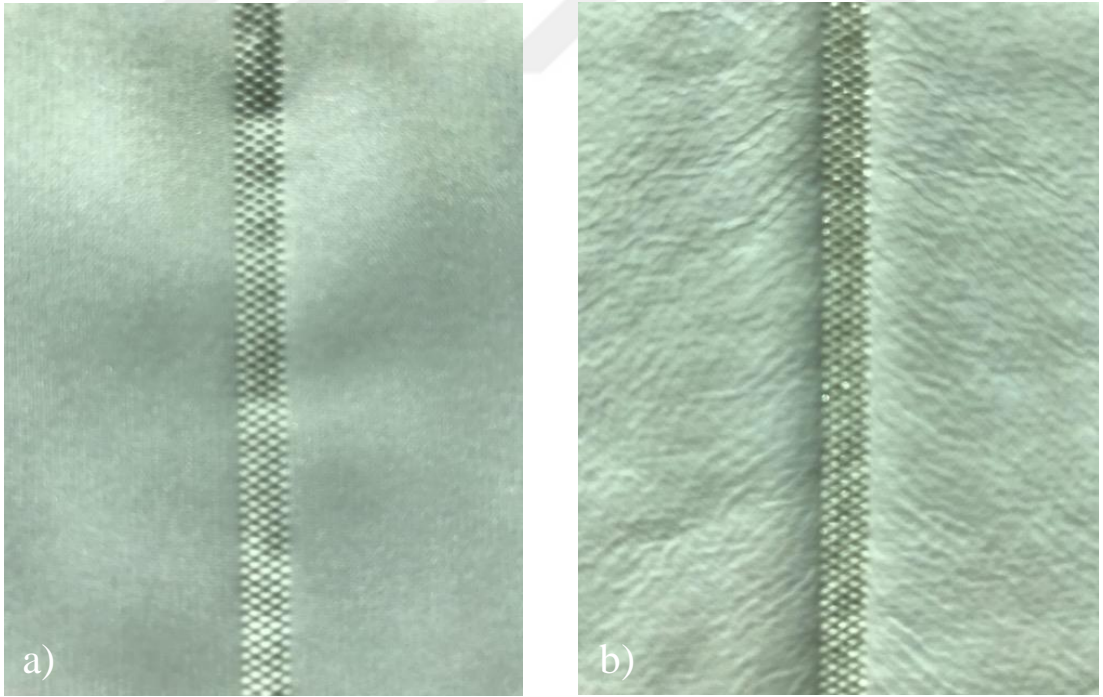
Ultrasonik dikiş makinesinde R1 ile dikilen O3 kumaşının görüntüsü
